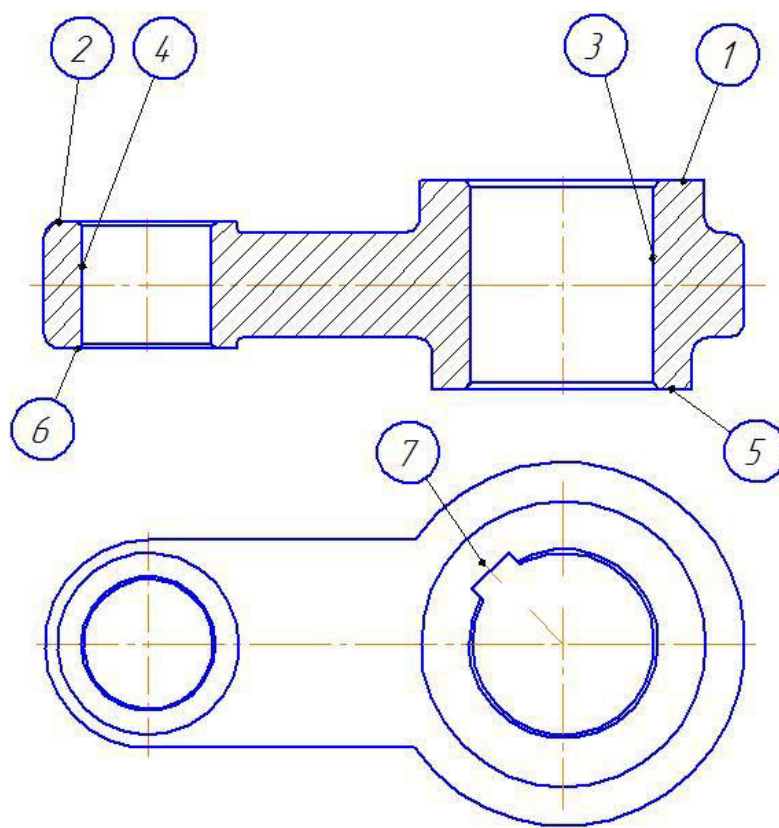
Эскиз детали с нумерацией поверхностей
